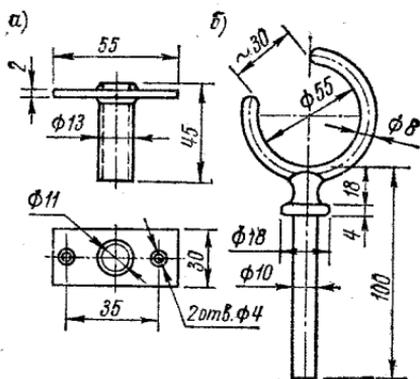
Подуключина (а) и уключина (б) сварной конструкции.
